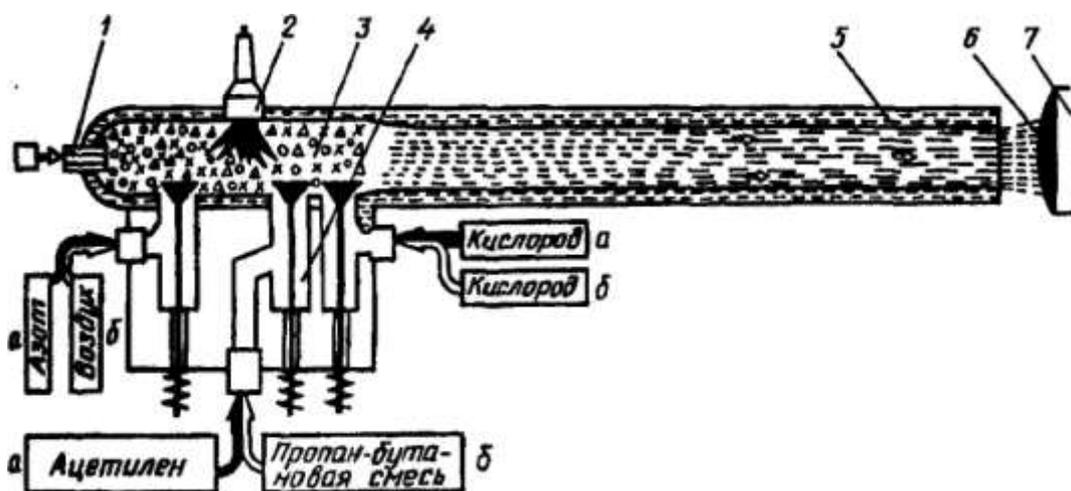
Схема установки для детонационного напыления: а – базовой; б – усовершенствованной; 1 – порошковый питатель; 2 – запальное устройство; 3 – взрывная камера; 4 – смесительная камера; 5 – водоохлаждаемый ствол; 6 – покрытие; 7- восстанавливаемая деталь
